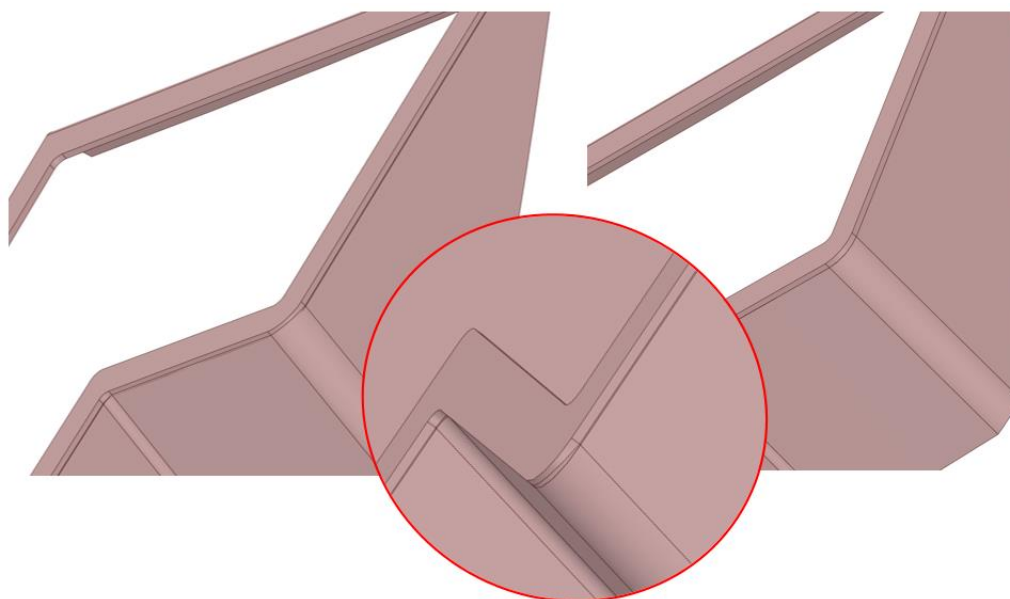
Příklad řešení problematiky svarových spojů.
